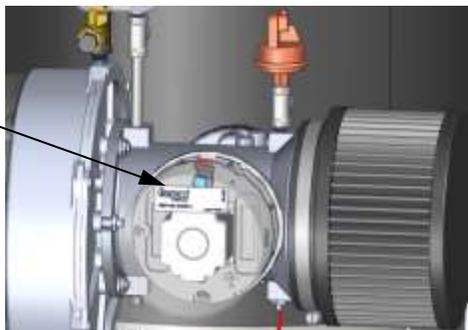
Emplacement typique du couvercle de soupape d'air/carburant
